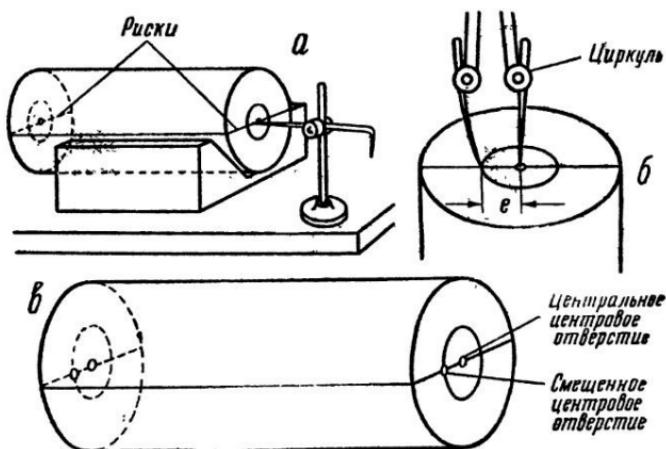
Подготовка заготовки для эксцентричного точения: а — разметка основного диаметра; б — нахождение центра эксцентричной окружности; в — заготовка, зацентрованная для симметричного и эксцентричного точения.
